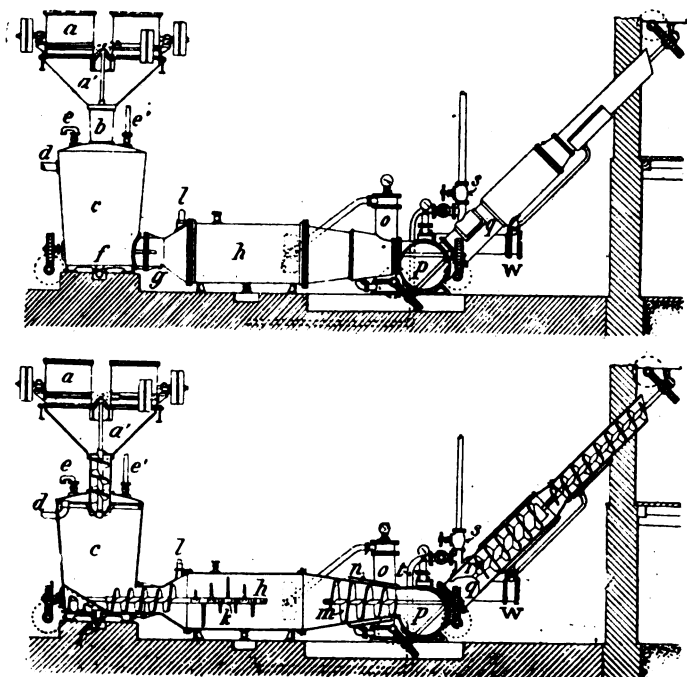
et 2. — Élévation et coupe longitudinale du diffuseur.
